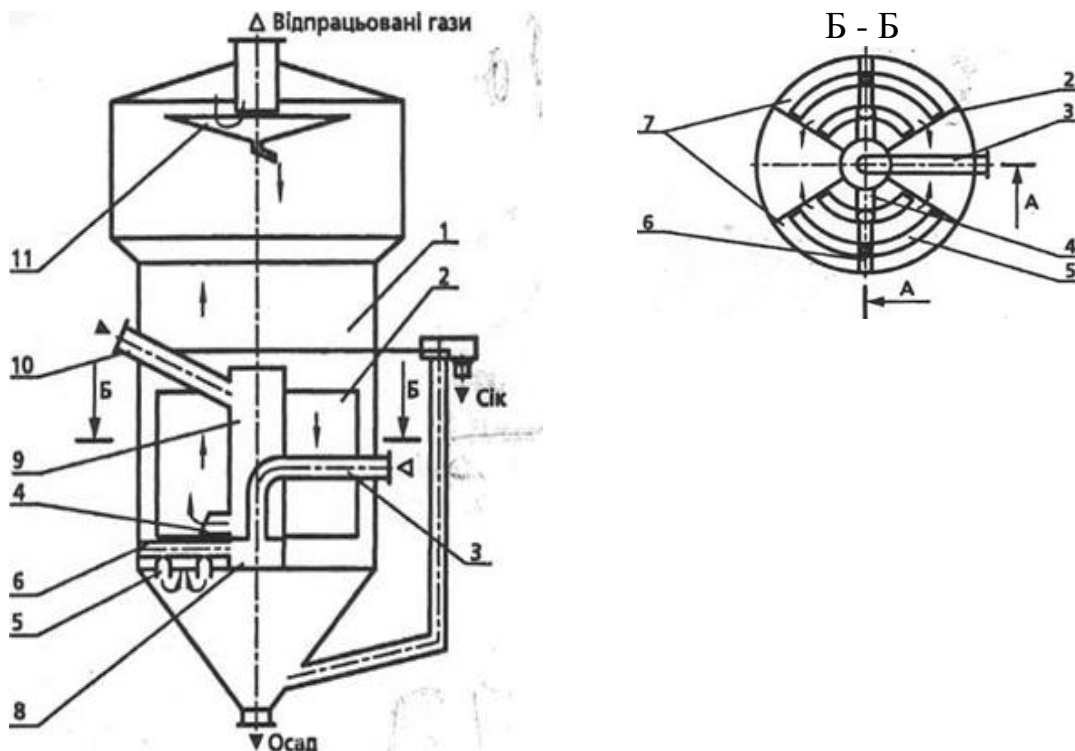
Сатуратор з радіальним розташуванням перегородок в корпусі 1 – циліндрично-конічний корпус; 2 – перегородки; 3 – трубопровід подачі газу; 4 – патрубки; 5 – барботер; 6 – направляюча; 7 – секції; 8 – колектор; 9 – труба; 10 – трубопровід подачі соку; 11 – сепаратор.
